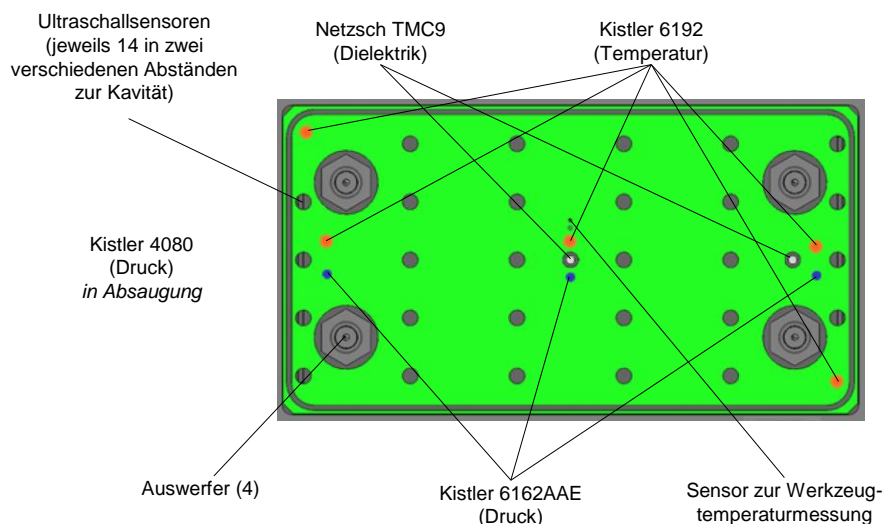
Finales Sensorkonzept im Plattenwerkzeug
